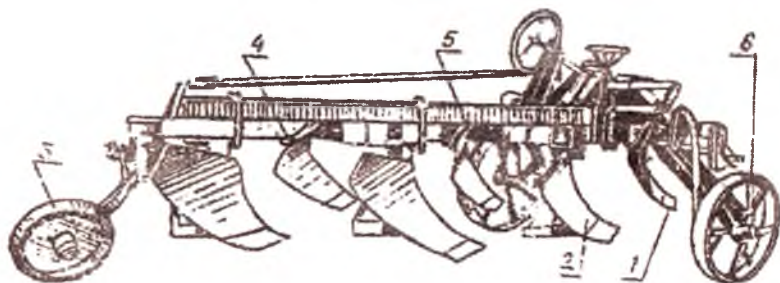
Общий вид плуга двухъярусного трехкорпусного ПЯ-3-35.
